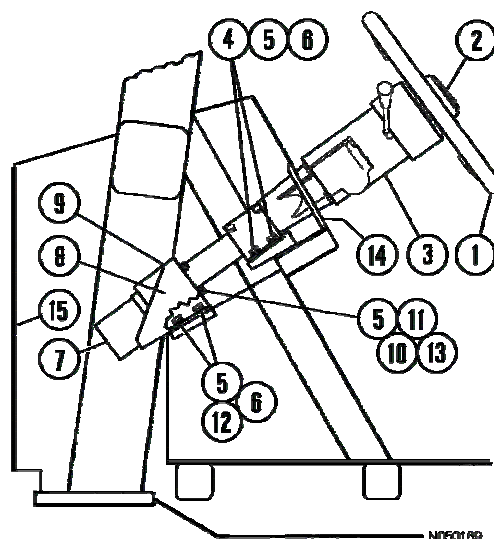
MONTAJE DE LA COLUMNA DE LA DIRECCION
